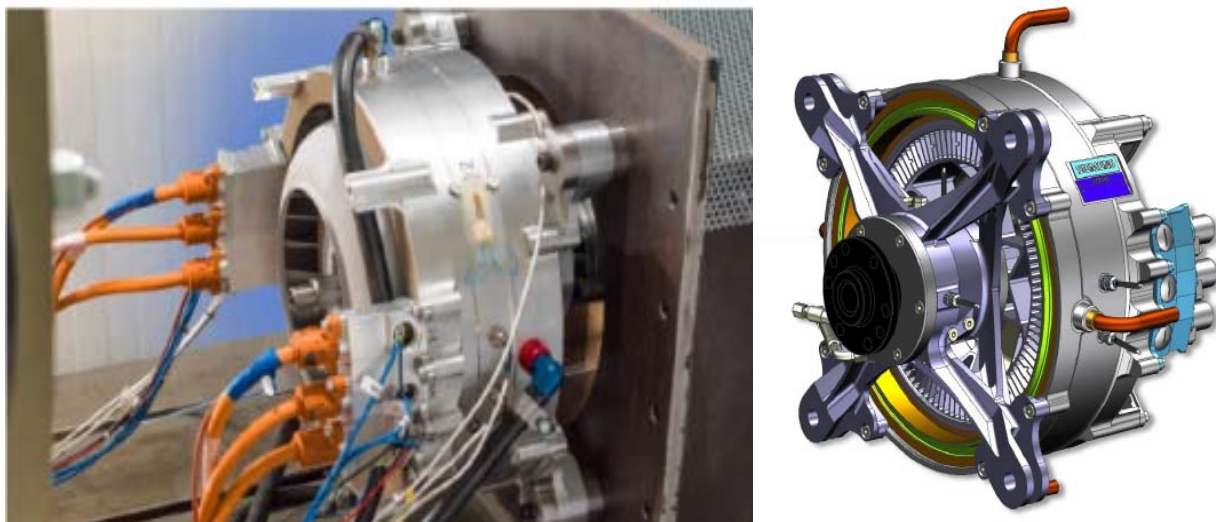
Внешний вид и модель двигателя мощностью 261 кВт (*Siemens*)
